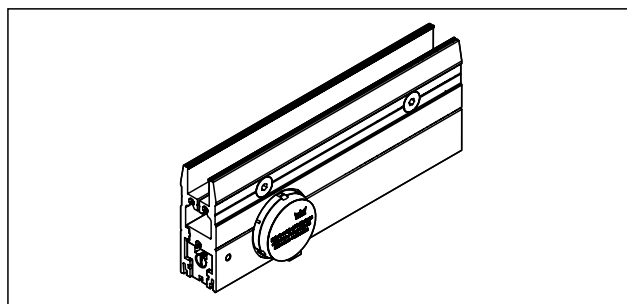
Riegelschloss mit Mikroschalter in Ausführung links, für KABA-Rundzylinder
